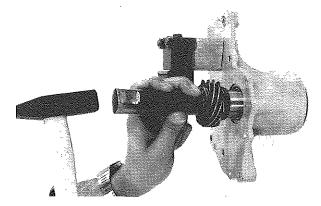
Ingranaggio comando spinterogeno Distributor control gear
